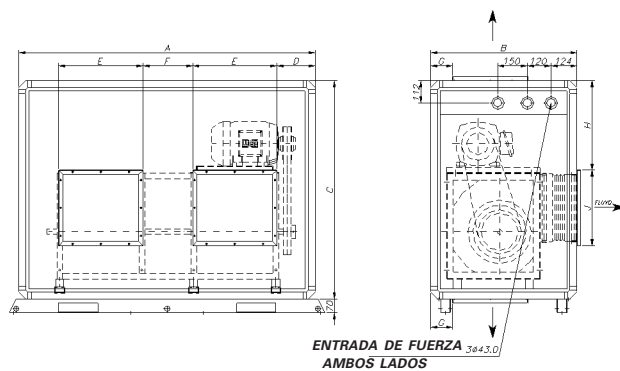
Dimensiones Módulo Ventilador 050 a 100
